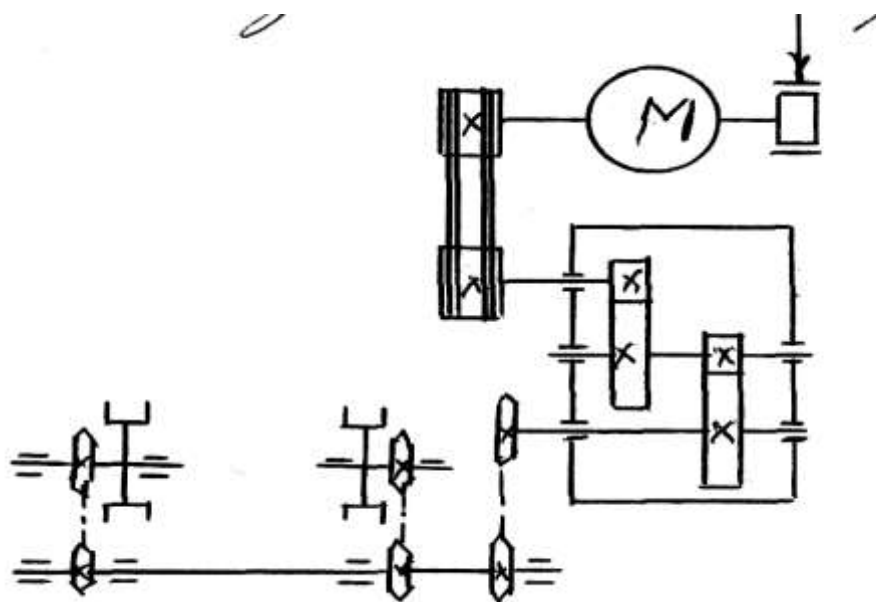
Кінематична схема пересування візка бетоноукладача.
